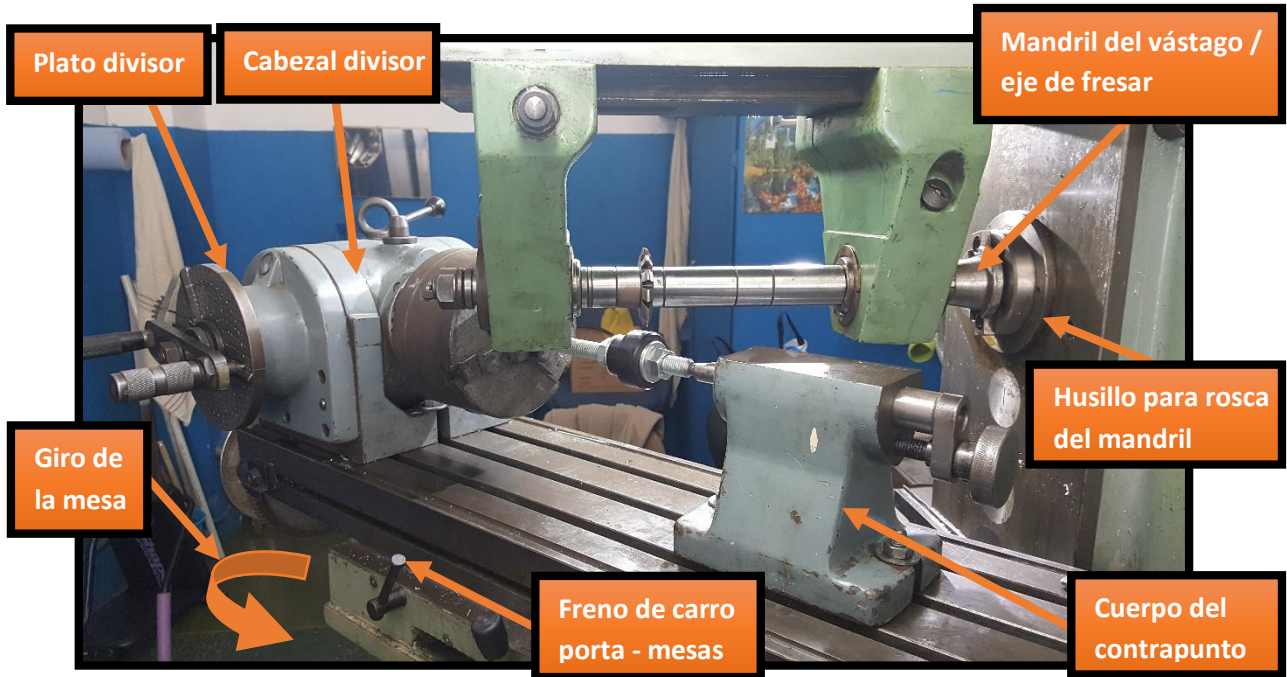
Disposición de una fresadora universal con soporte.
